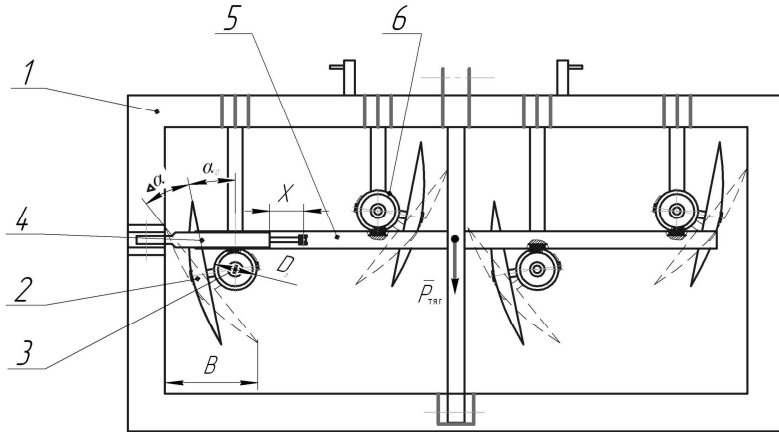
Схема модернізованого дискового підгортальника: 1 - рама, 2 - дискові робочі органи, 3 – стійка з вертикальною віссю, 4 - гідроциліндр, 5 - тяга, 6 - зубчасті колеса
